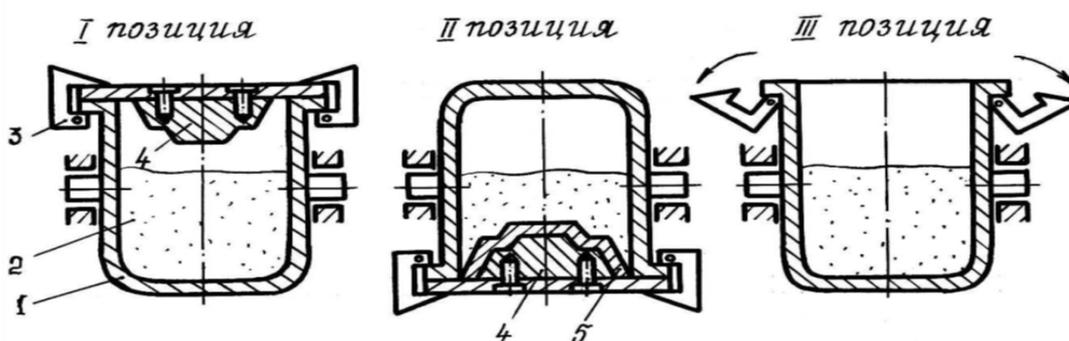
Бункерный способ изготовления оболочковых полуформ
